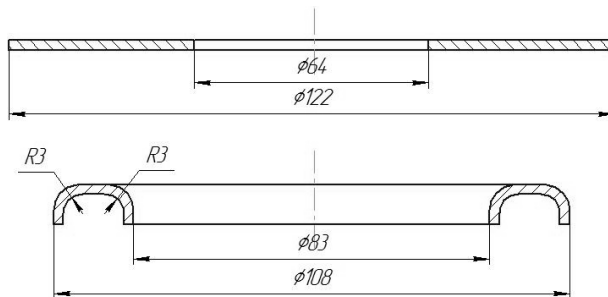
Геометрические размеры заготовки и кольцевого образца
